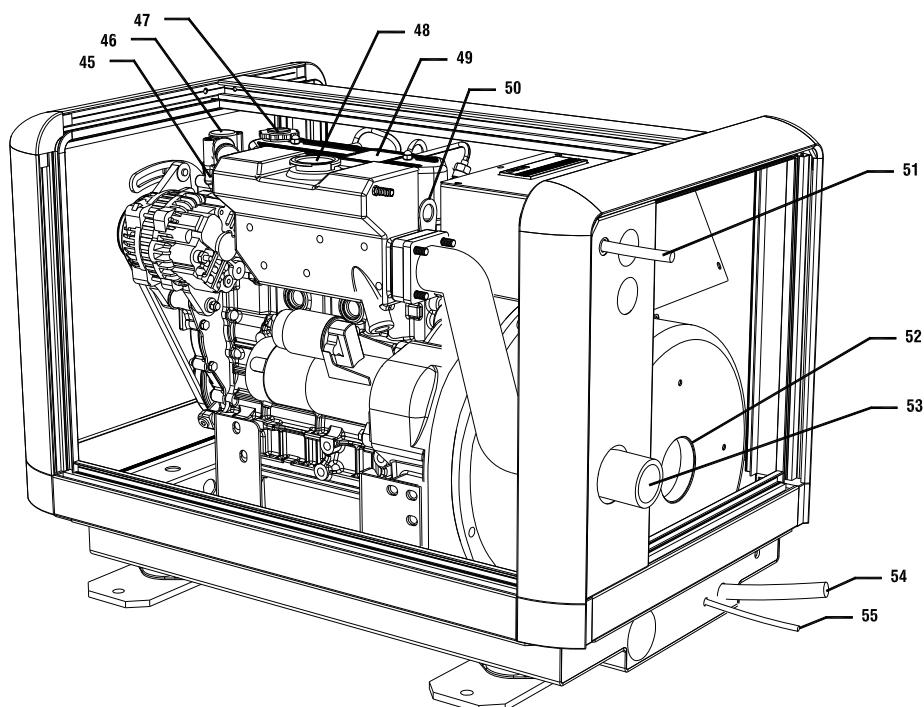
Vue arrière des composants principaux du Whisper 6 et 10
